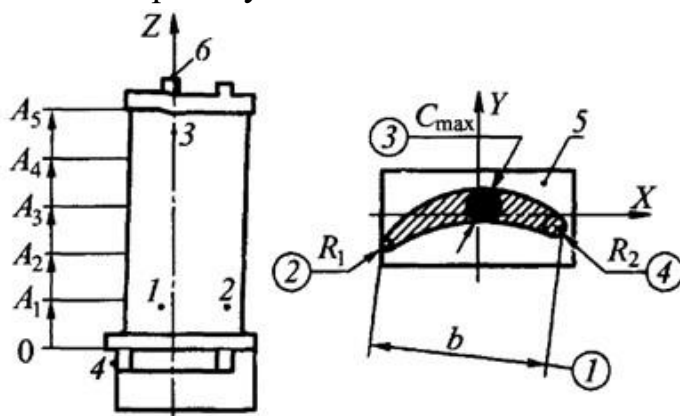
схема контролю й доопрацювання заготовки на операціях вхідного контролю: 1...6 – базові точки заготовки.
